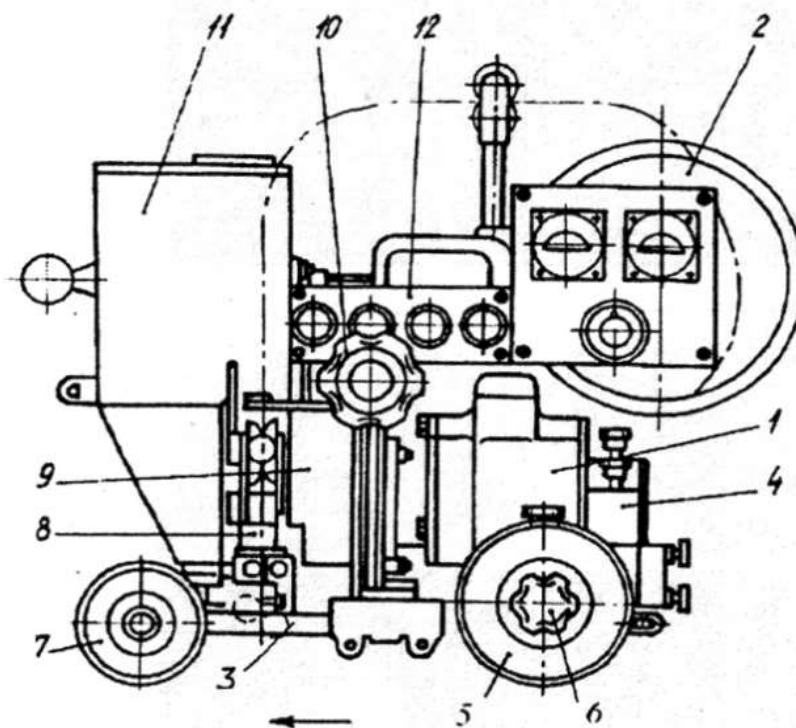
Конструкция сварочного трактора АДФ-1002
